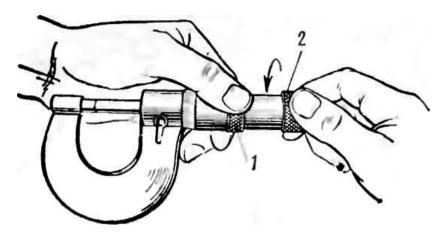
Микрометр завода «Калибр»: 1 – барабан; 2 – корпус трещотки
